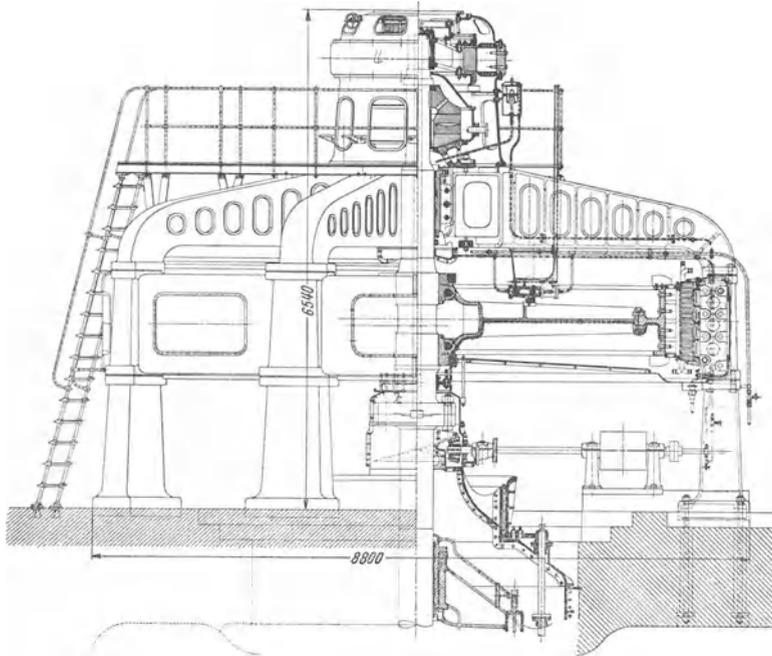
Wasserkraft-Drehstromerzeuger auf Fundamentfüßen für niedrige Drehzahl; schmale Maschine — großer Durchmesser. 7 MVA, 8,4 kV,  $n = 83,3$  U/min.
